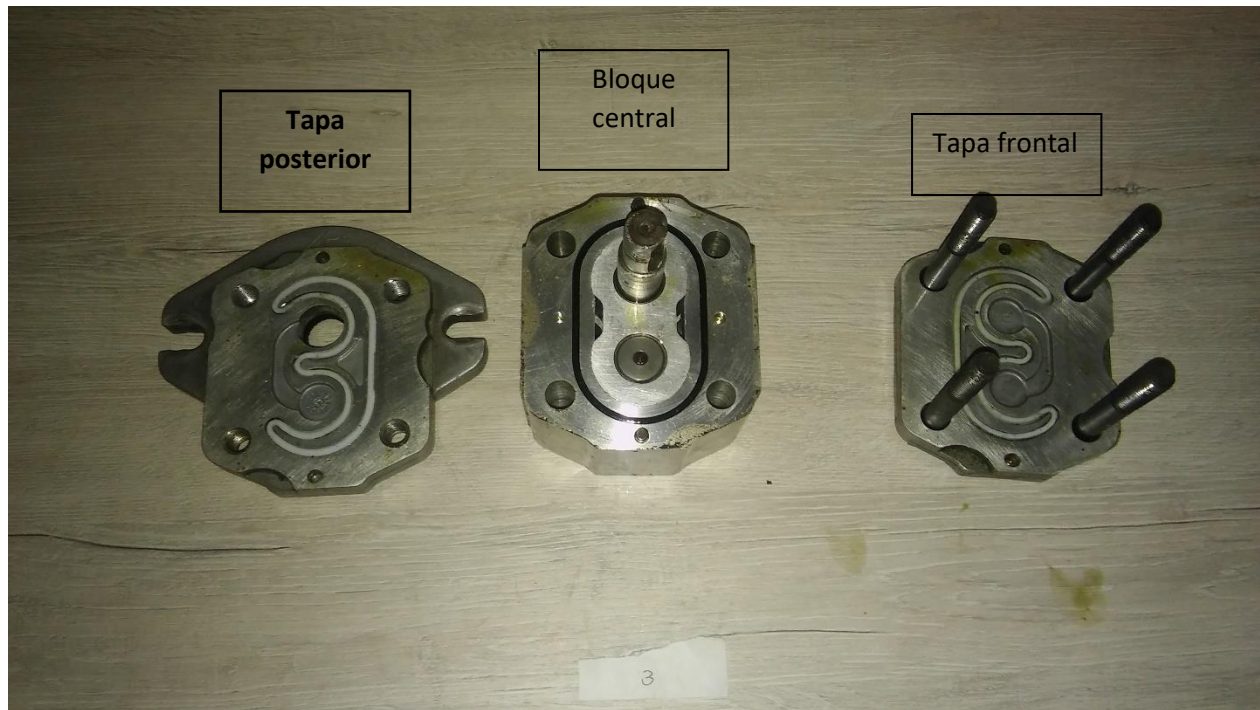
Bomba de engranajes desarmada y partes constituyentes
